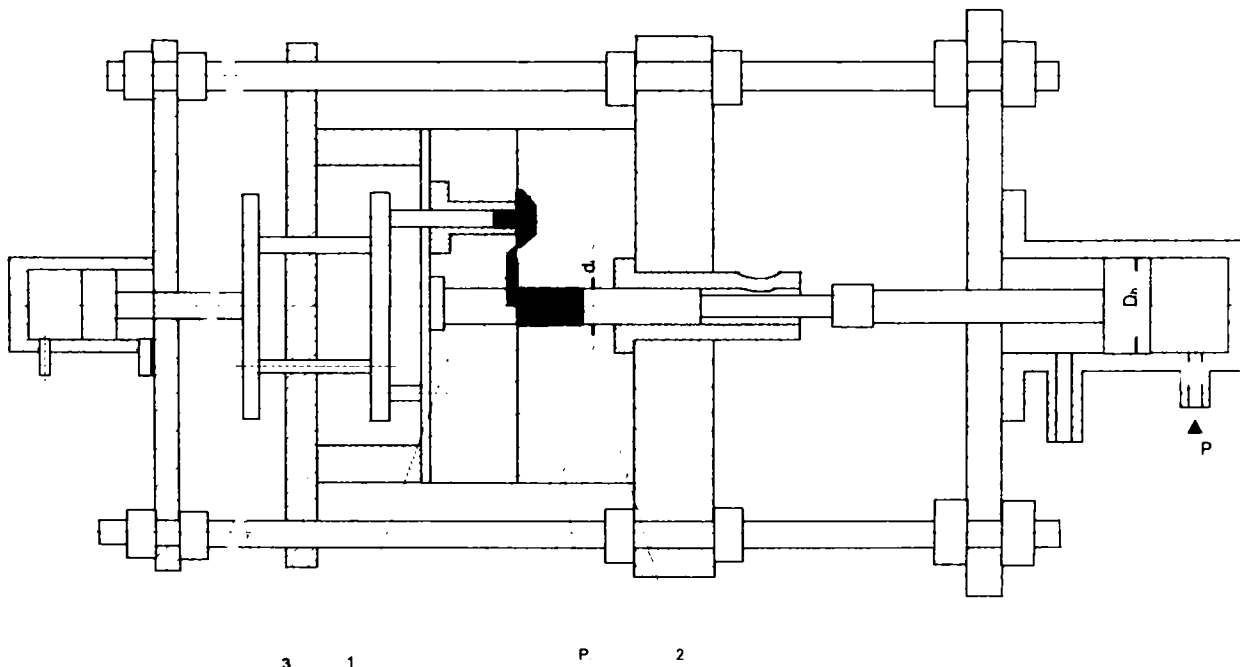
Schema sistemului piston hidraulic – piston injectare:
